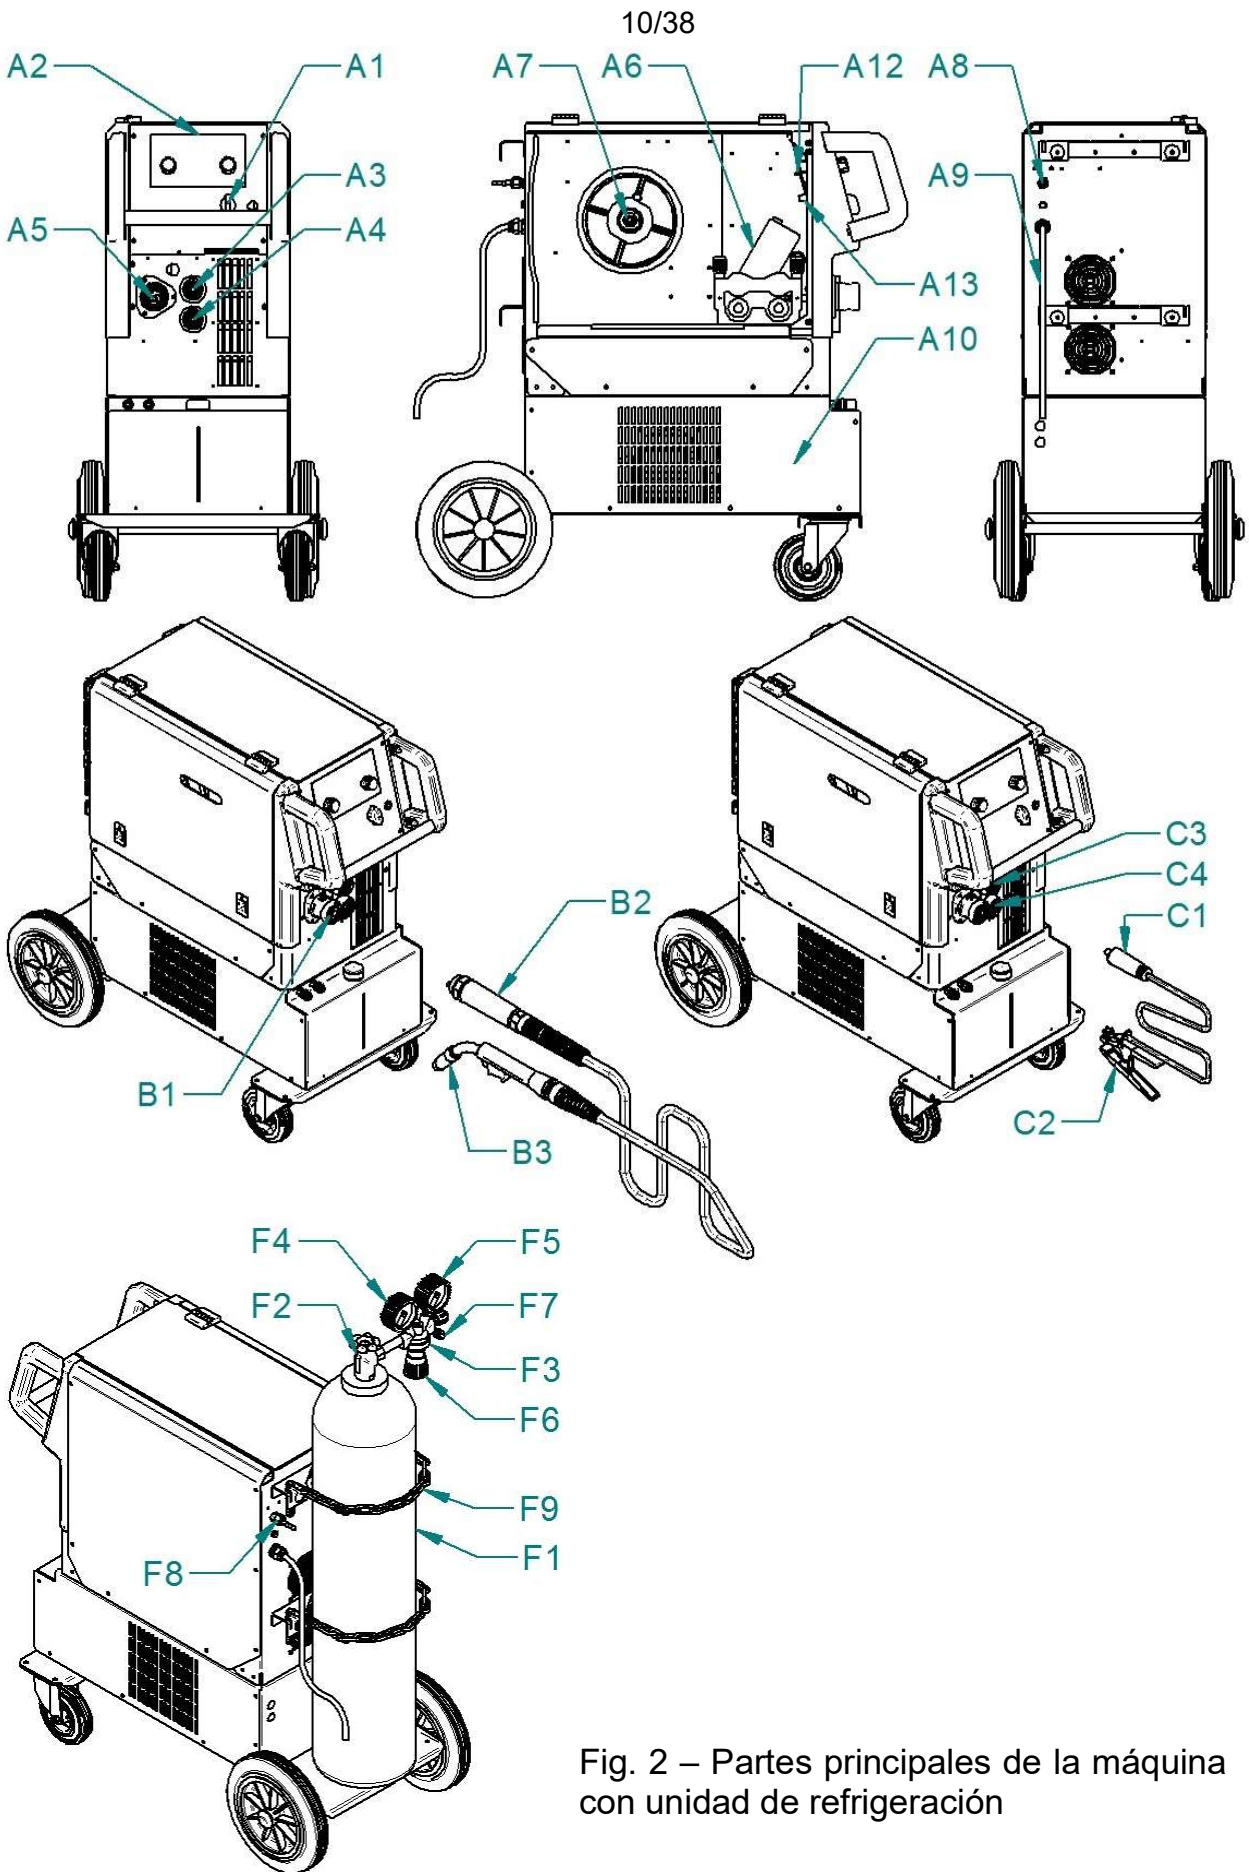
Partes principales de la máquina con unidad de refrigeración
